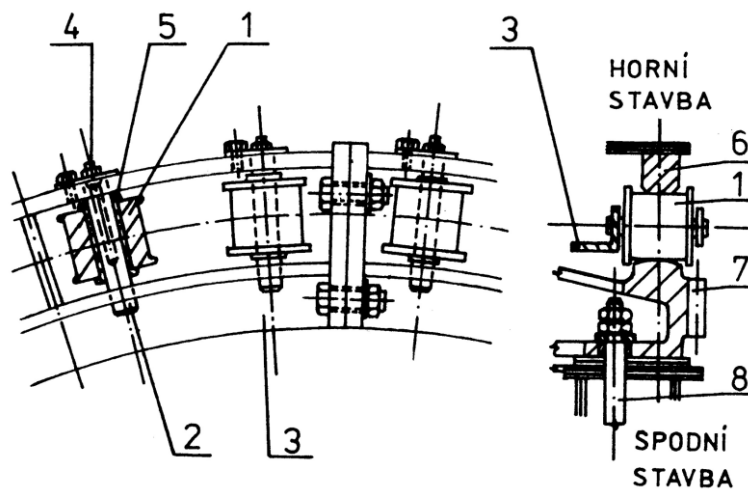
Systém otoče horní stavby s kruhovou kolejničí
